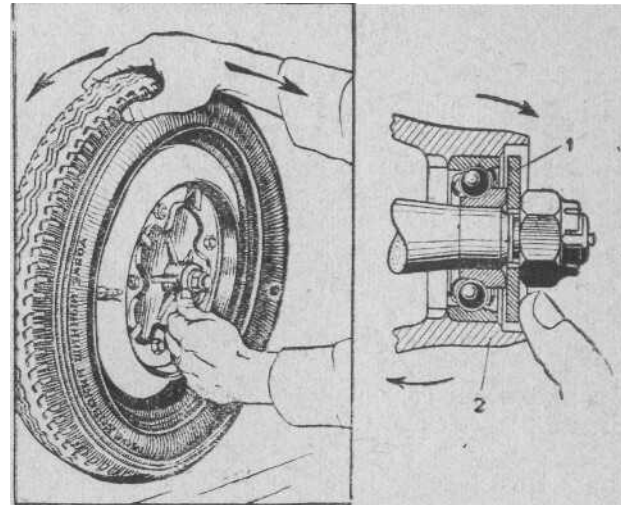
Проверка регулировки подшипников ступиц передних колес
